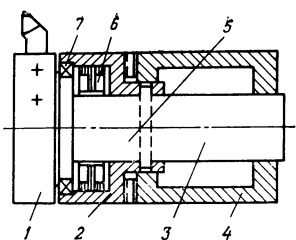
Поворотная резцедержавка со встроенным МДМ
